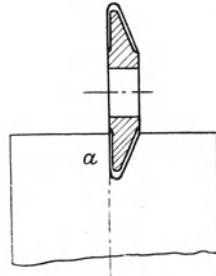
Das Fräsen der Nuten für hinterdrehte Stirnzähne.
